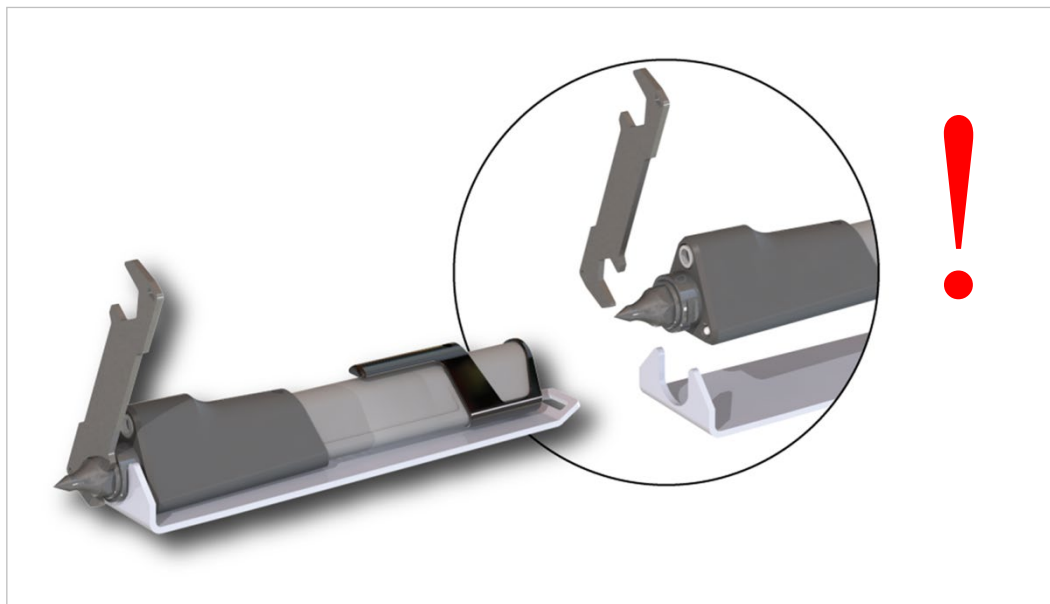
Montage und Demontage der Waveguides mit dem Schlüsselsatz BS-20
